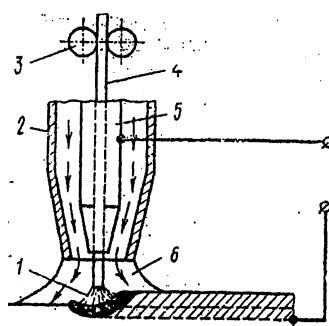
Дуговая сварка в защитных газах плавящимся электродом:
